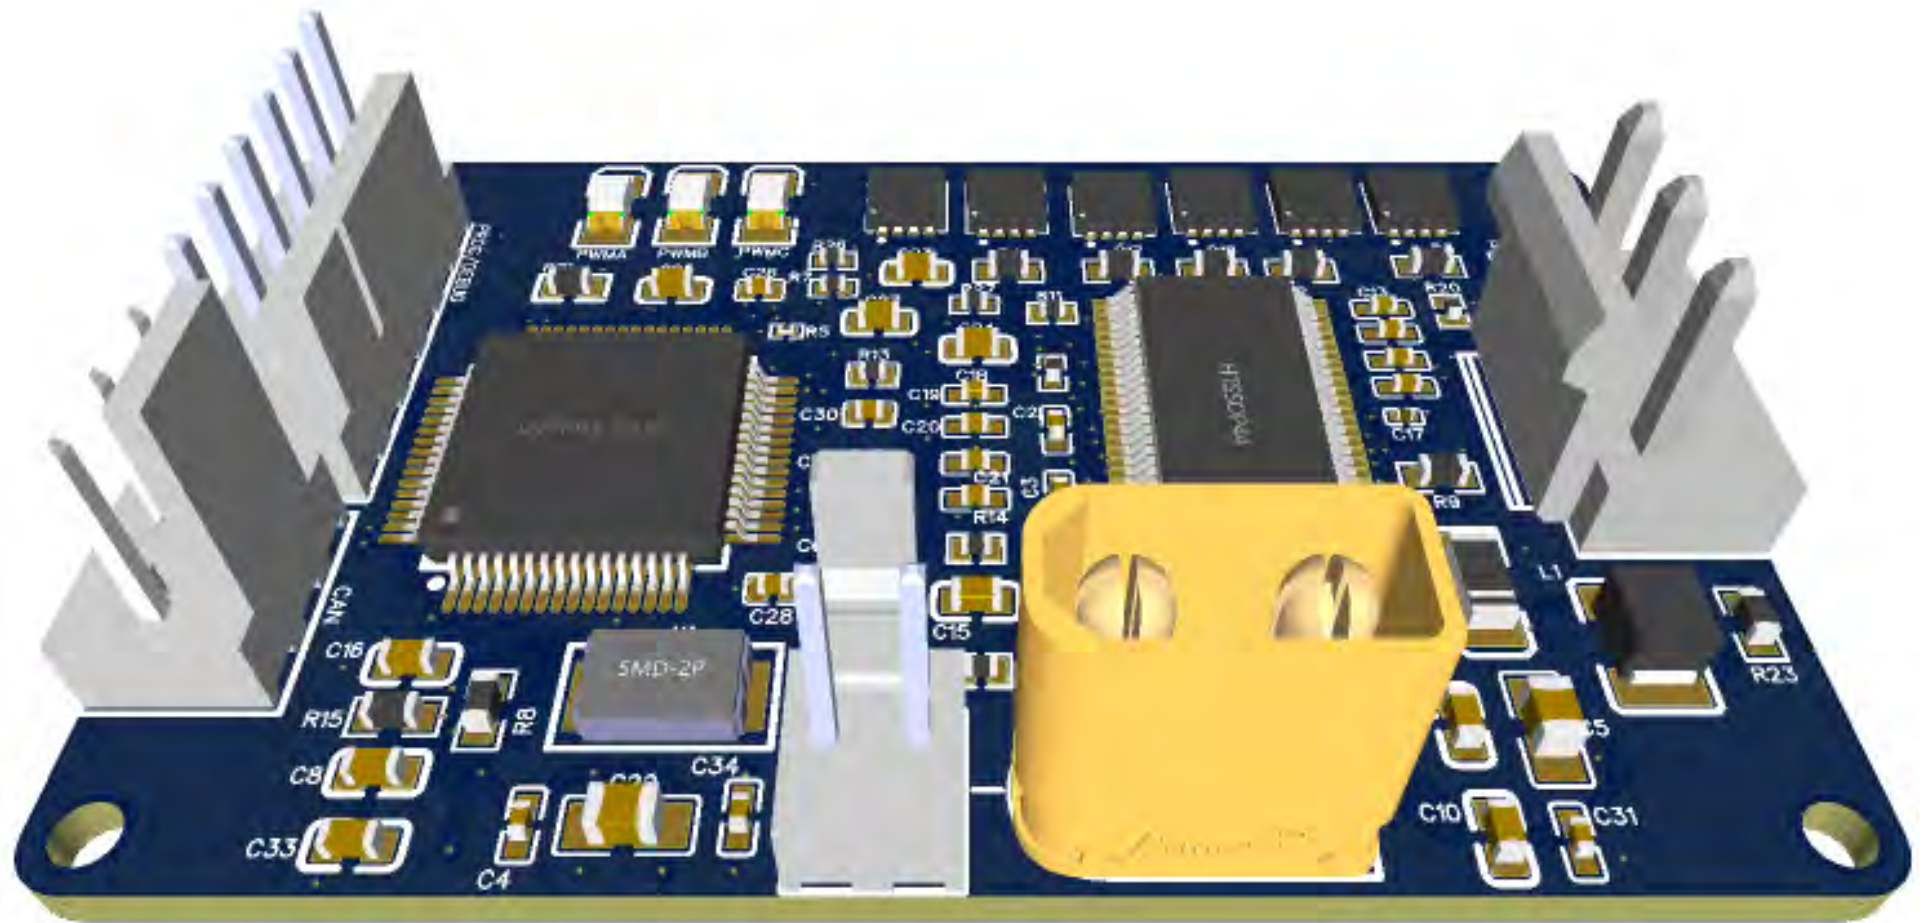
Modelado 3D de la tarjeta PCB – capa superior
